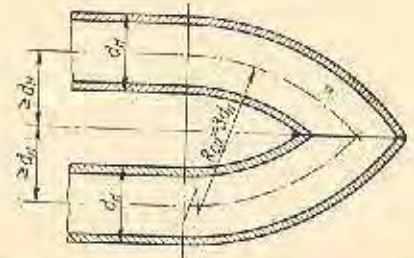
Конструкция сварного поворота трубы на 180° с малым расстоянием между параллельными ветвями ее
